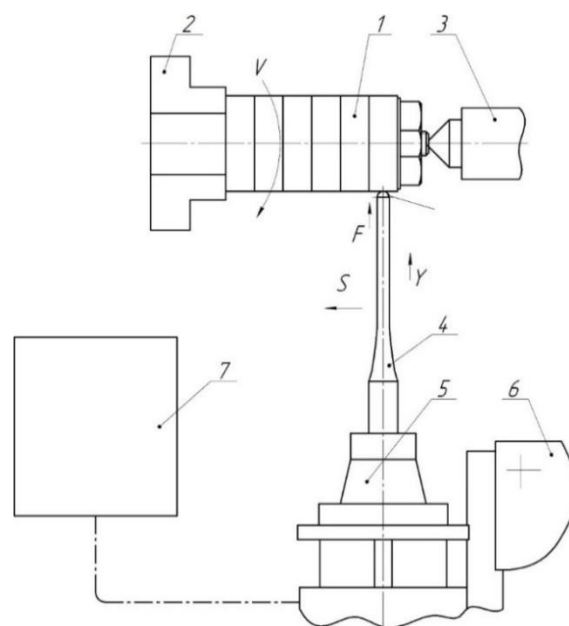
Схема ультразвуковой упрочняющей обработки: 1 – заготовка; 2 – патрон; 3 – задний центр; 4 – ультразвуковой инструмент с полуцилиндрическим наконечником; 5 – магнитострикционный преобразователь в корпусе ДТМ; 6 – резцедержатель токарного станка; 7 – ультразвуковой генератор
